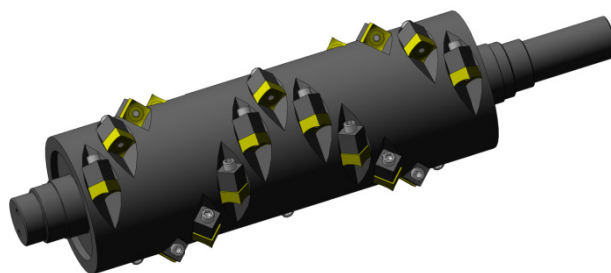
3D-модель сборочной единицы «Ротор» из сборки «Корпус шредера»
